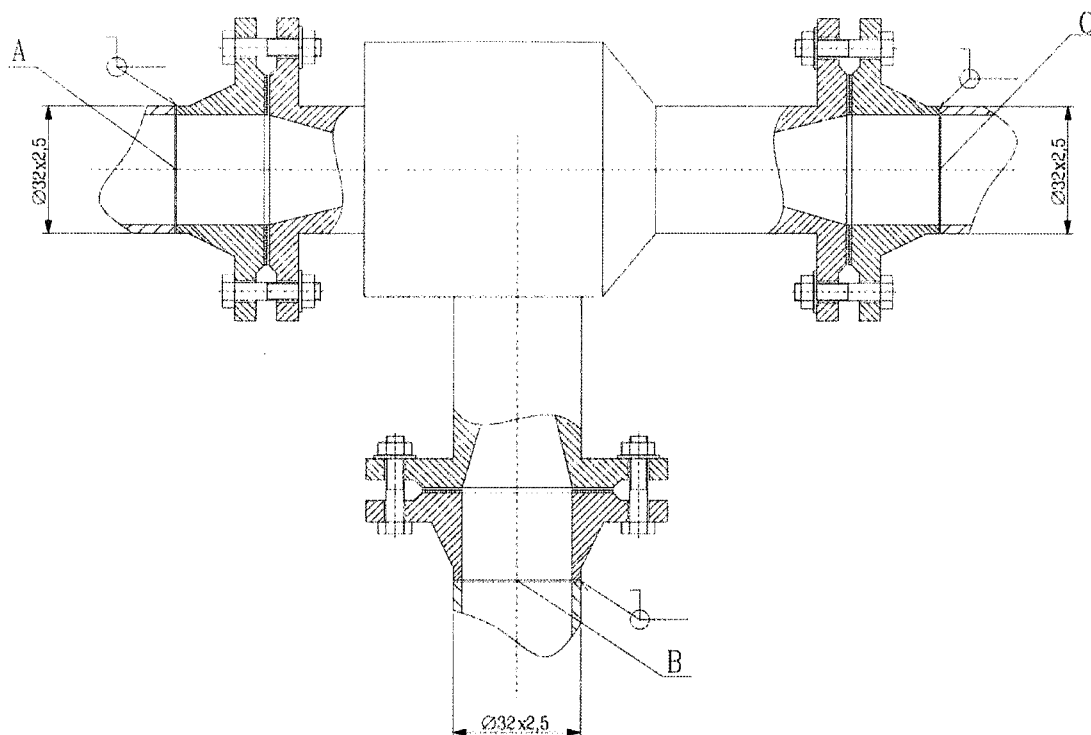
Габаритный чертеж эжектора приема гидразина QCE10BN001
